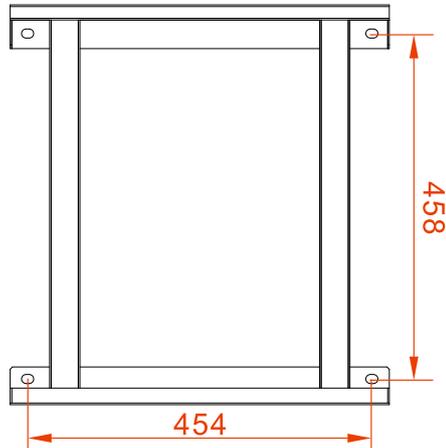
Dimensioni dei fori di installazione del supporto (unità di misura: mm)
